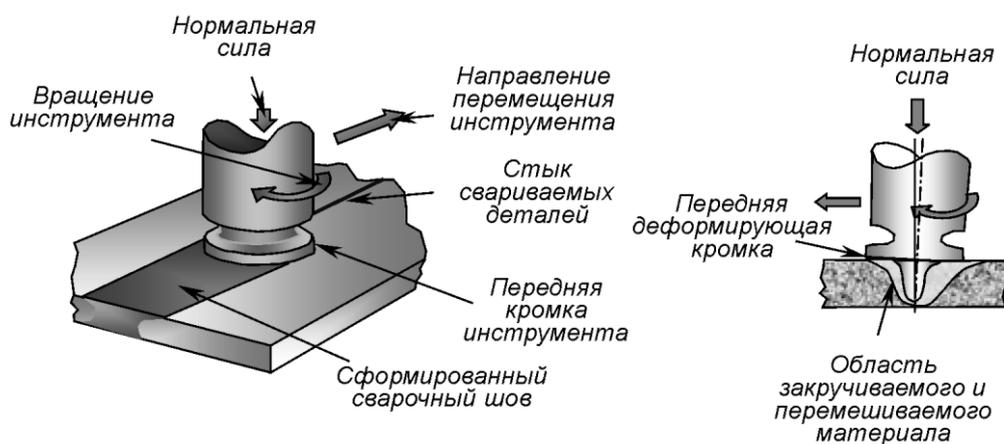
Схема процесса сварки трением с перемешиванием [1].
